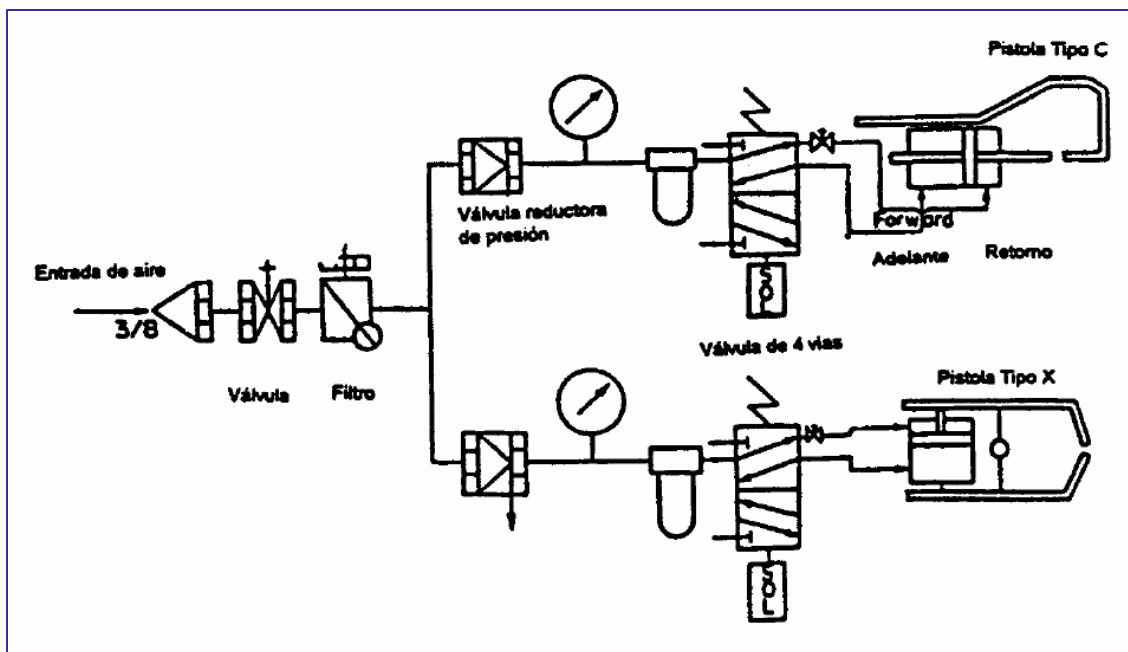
Circuito de aire comprimido para un equipo soldador con dos pistolas
